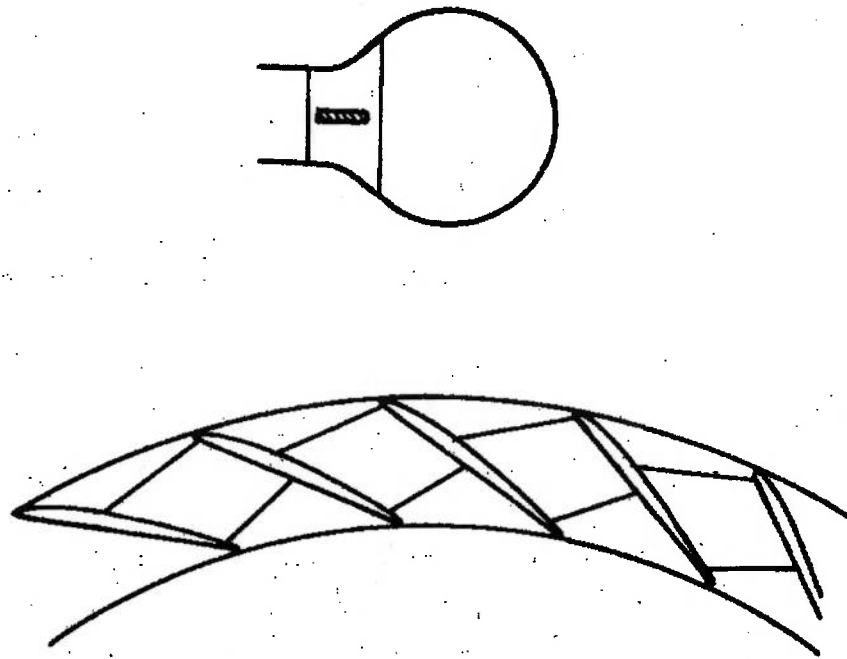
Placas amortecedoras – vista em corte e planta [13].
